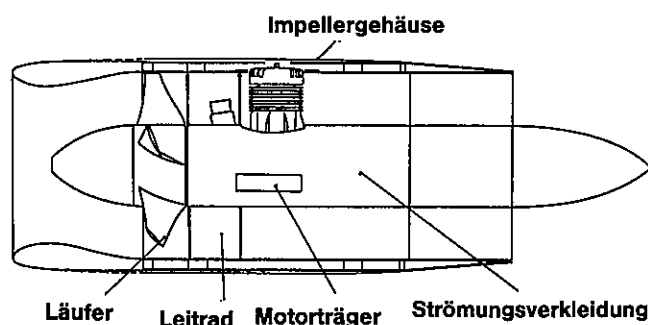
Skizze: Hauptbaugruppen des Impellers
